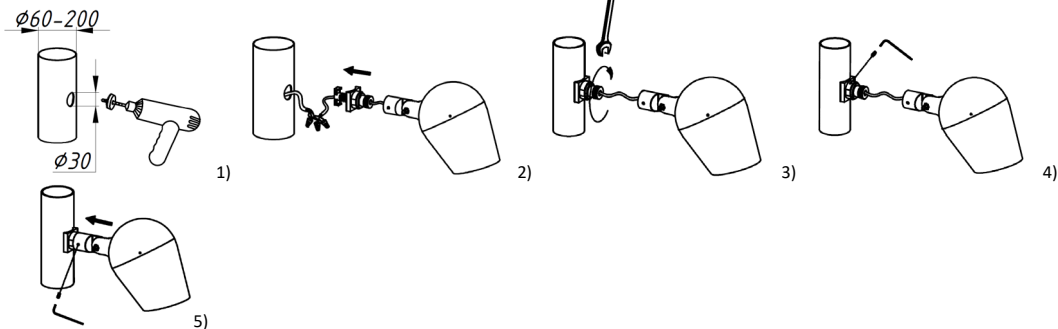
Установка на крепление к опоре скрытого монтажа арт.90900.
